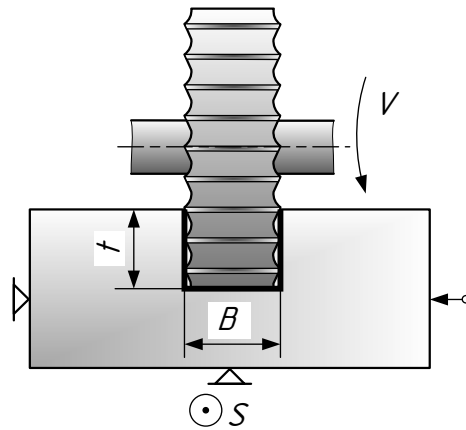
Обработка прямоугольного паза дисковой прорезной фрезой
